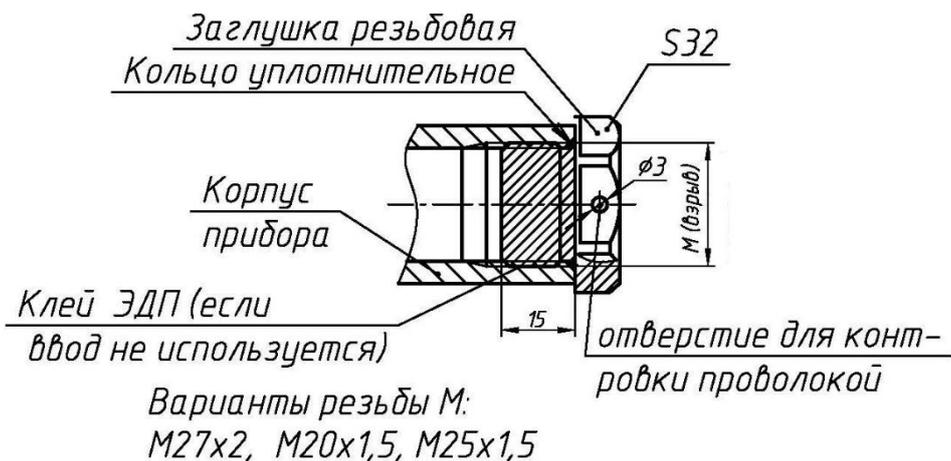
Элементы взрывозащиты при поставке оповещателя с резьбовыми заглушками
